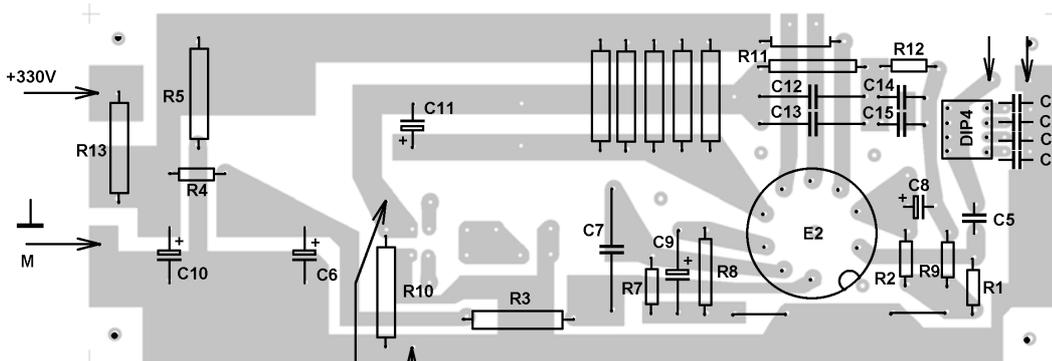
Deska s plošnými spoji linkových zesilovačů (86 x 180 mm)
